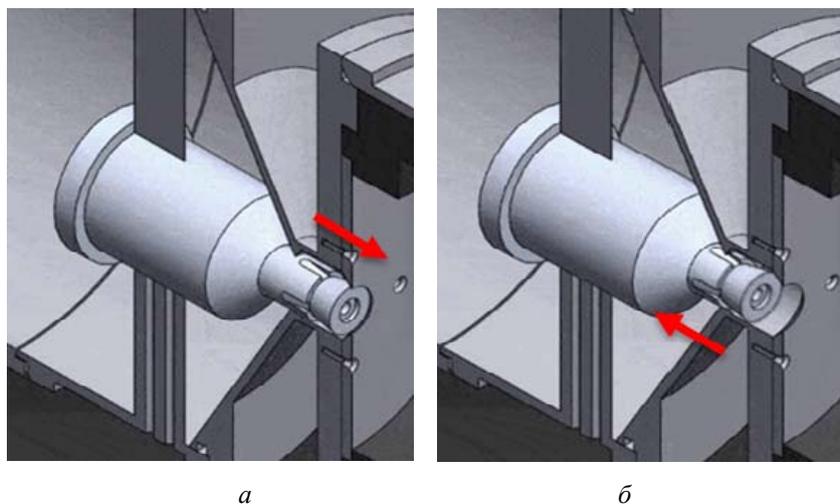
Запорно-регулирующий клапан системы подачи порошка металла: а – положение насадка «закрыто»; б – положение «открыто»
